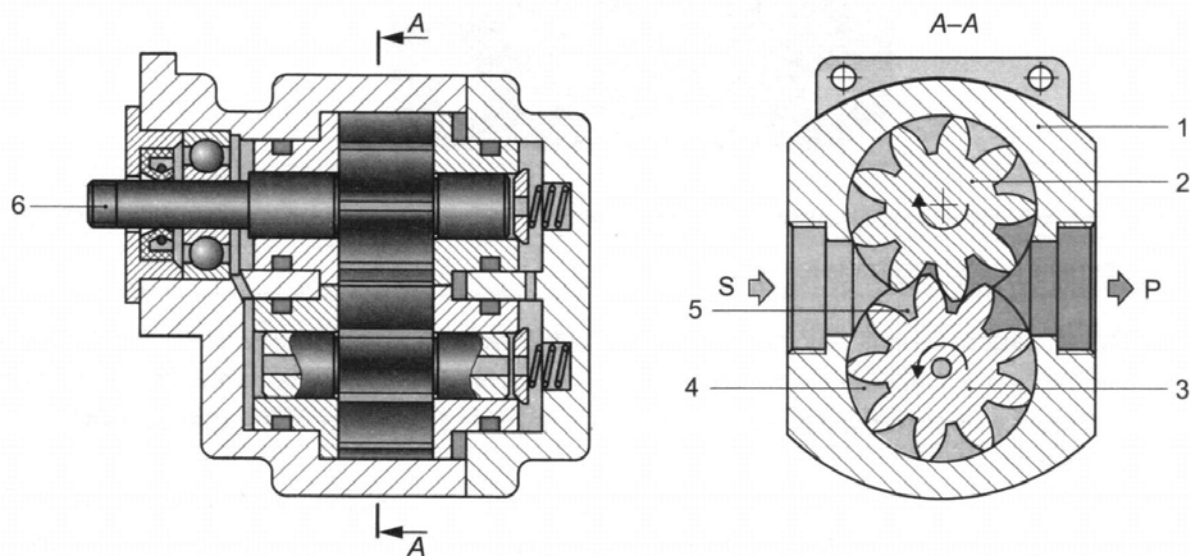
Шестеренный насос с внешним зацеплением [2]
